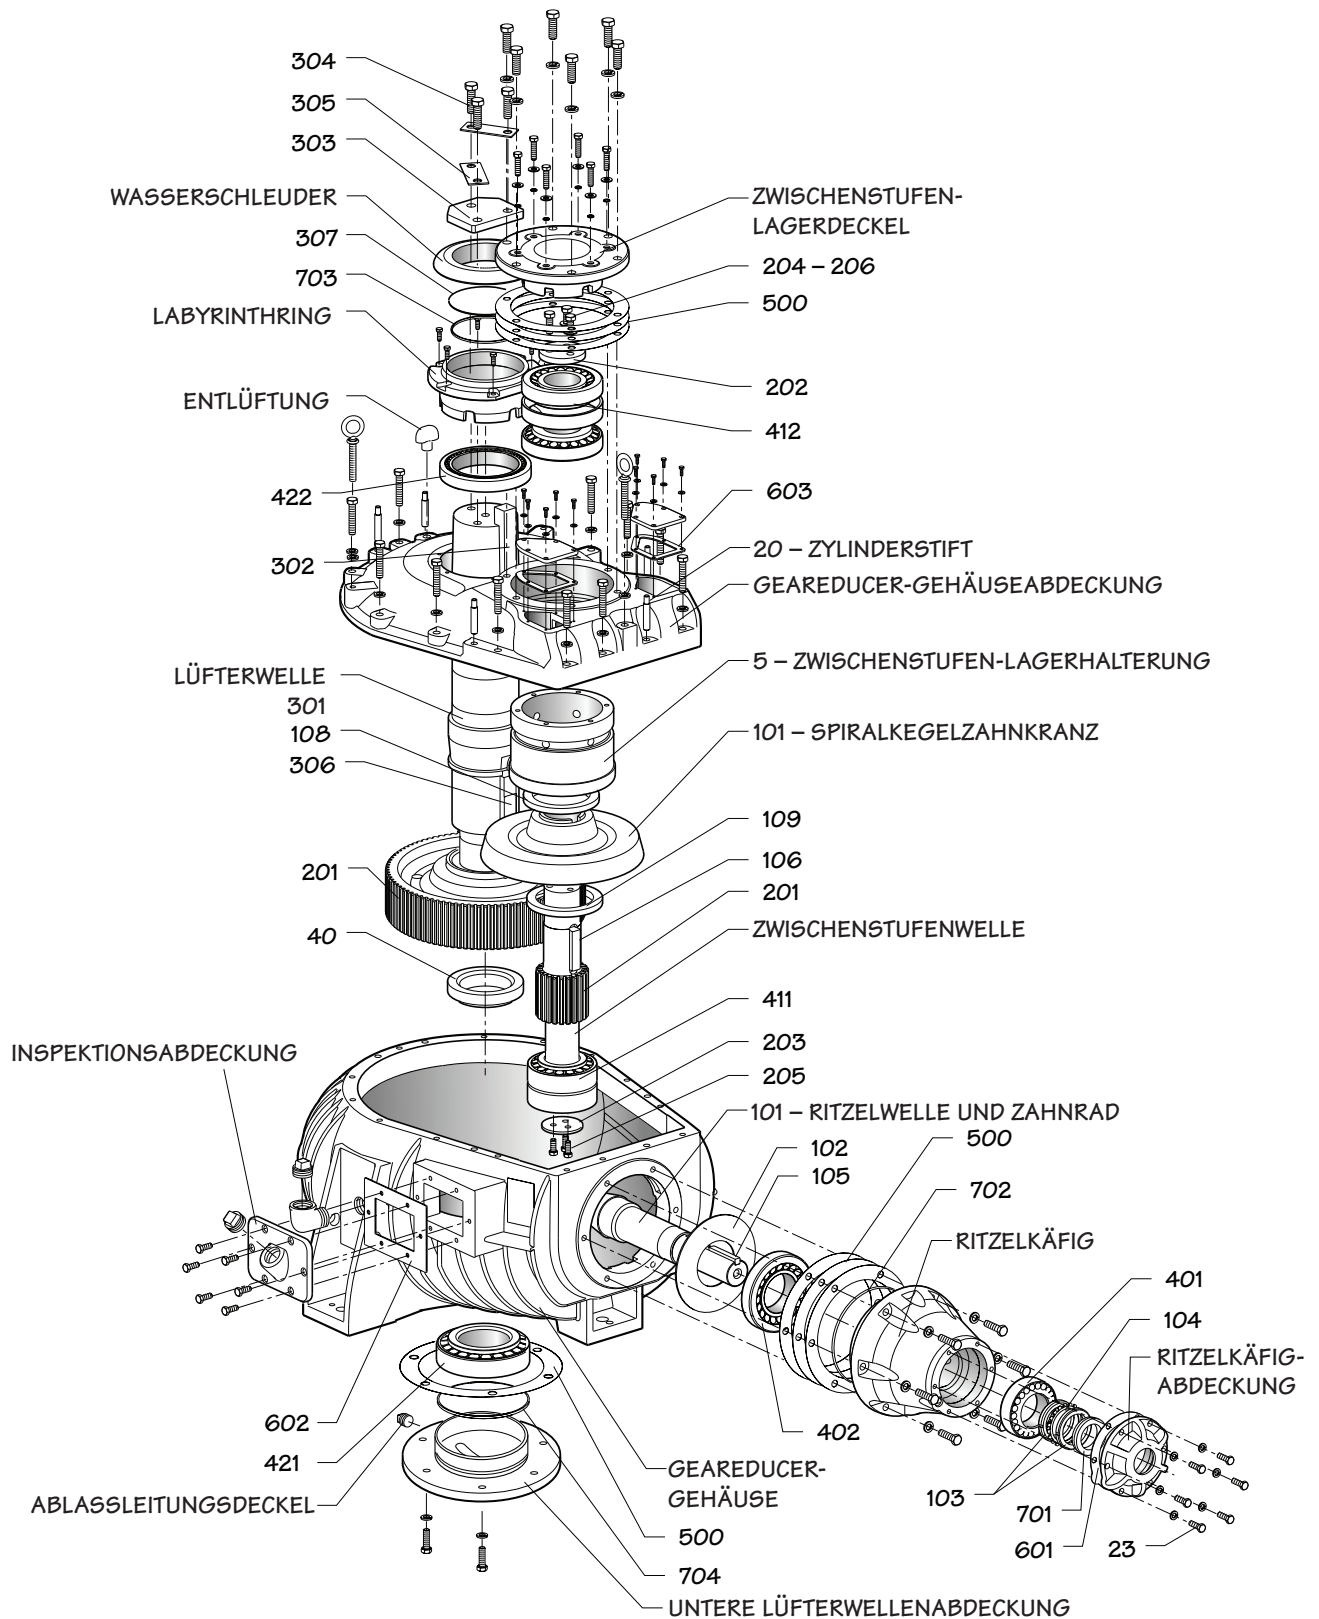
Modell 3400 Explosionszeichnung der Baugruppe Montage
